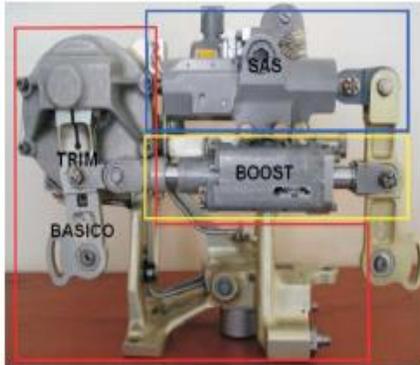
Subconjuntos del PITCH TRIM ACTUATOR ASSEMBLY.
